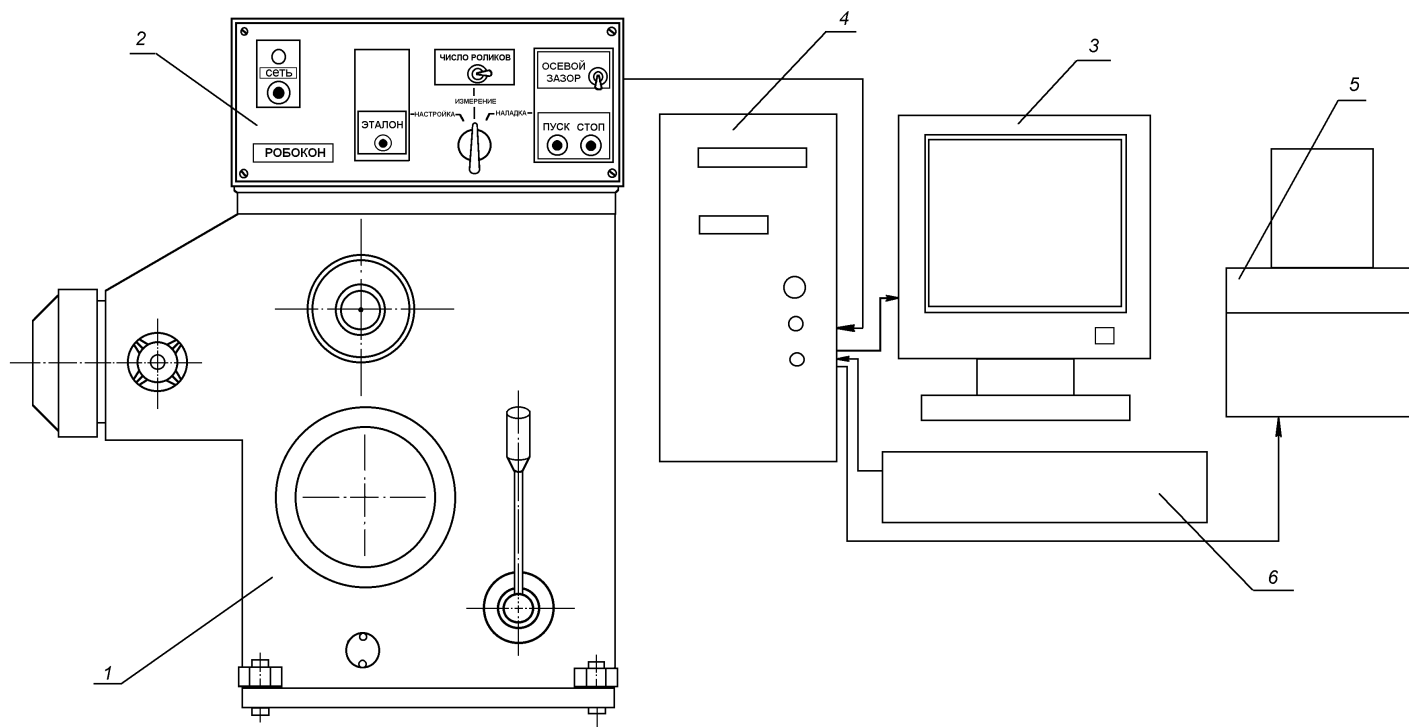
Полуавтоматический прибор для контроля блоков роликовых подшипников «РОБОКОН» модели 4156
